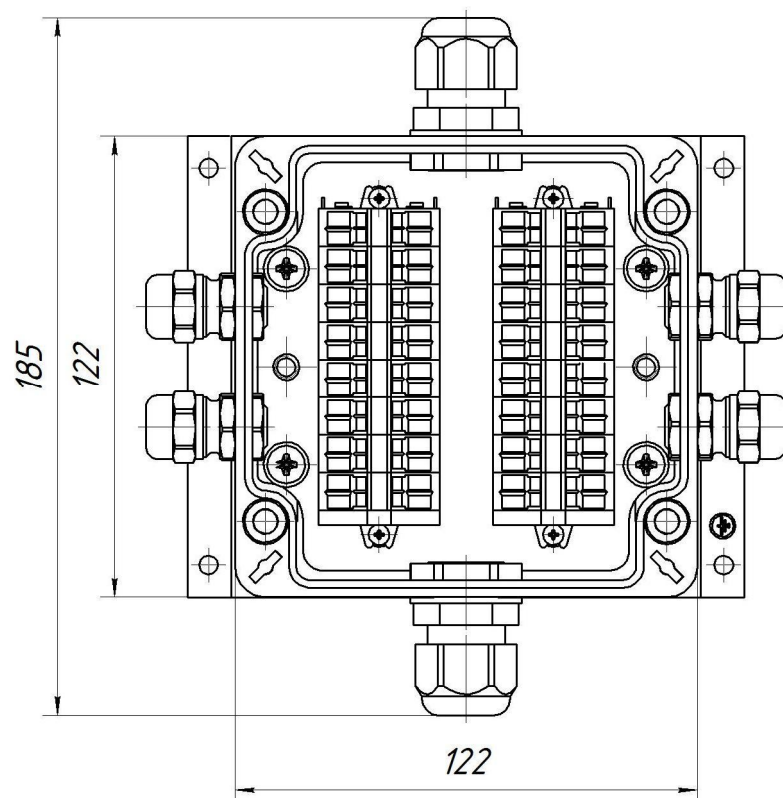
Вид клеммной коробки КК-4 без крышки
